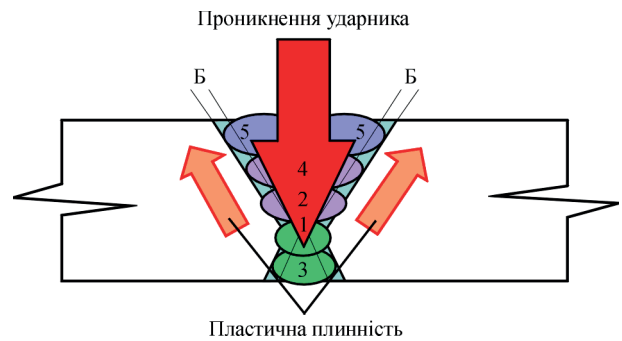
Схематичне зображення взаємодії металу комбінованого зварного шва з високошвидкісним ударником [9]: Б – буферний прошарок, наплавлений на крайки стика; 1–6 – послідовність зварювання шарів шва (1, 3, 5, 6 – аустенітна (нержавка) сталь, 2, 4 – зносоустійкий матеріал високої твердості)
